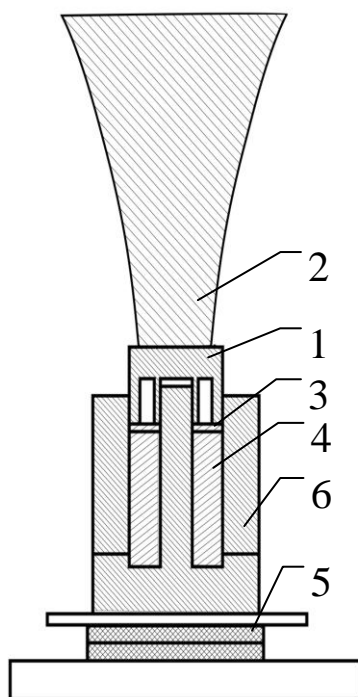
Схема процесса УЗ сварки изделия
